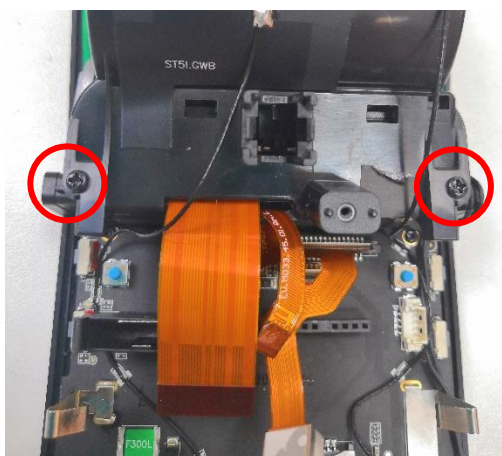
Саморезы, фиксирующие основание принтера и корпус верхний.
